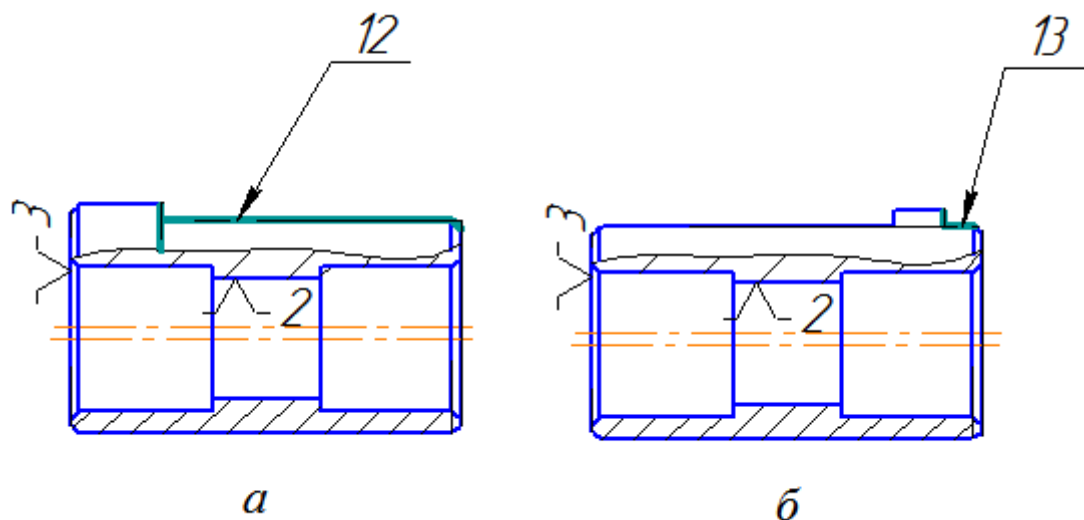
Эскиз токарной операции с ЧПУ 035
